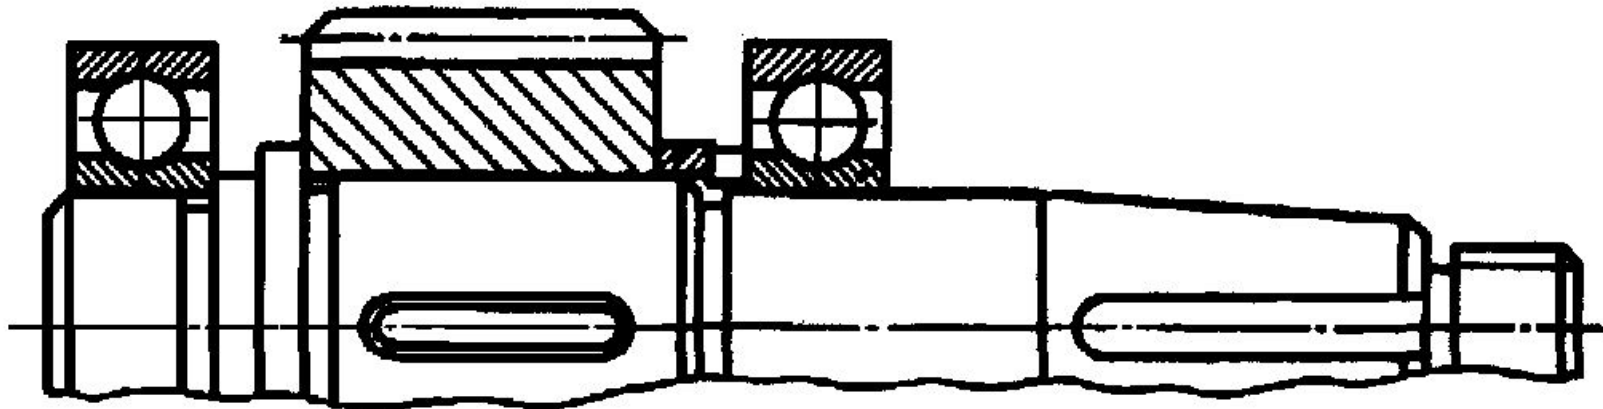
Вал цилиндрической передачи в сборе с шестерней и подшипниками качения.
